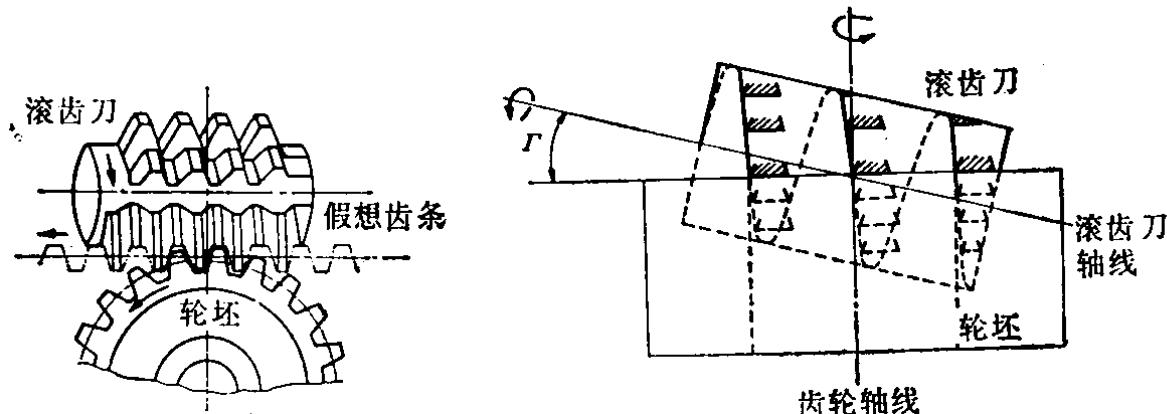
用滚齿刀滚制直齿轮    图 4-9 滚制直齿轮时滚齿刀的安装位置
